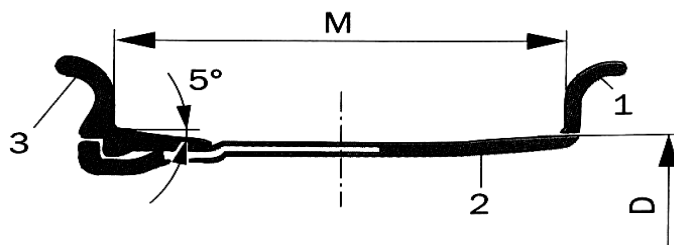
Конструкция разборного обода грузового автомобиля:
